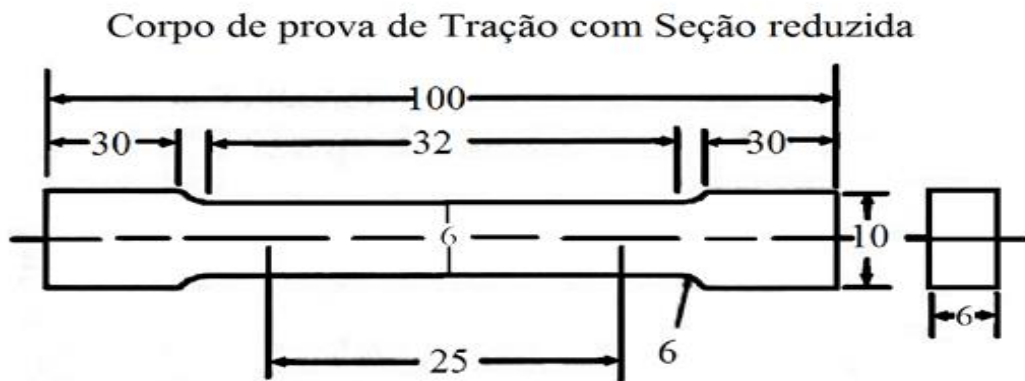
Dimensões do corpo de Prova de Tração com Seção Reduzida.
